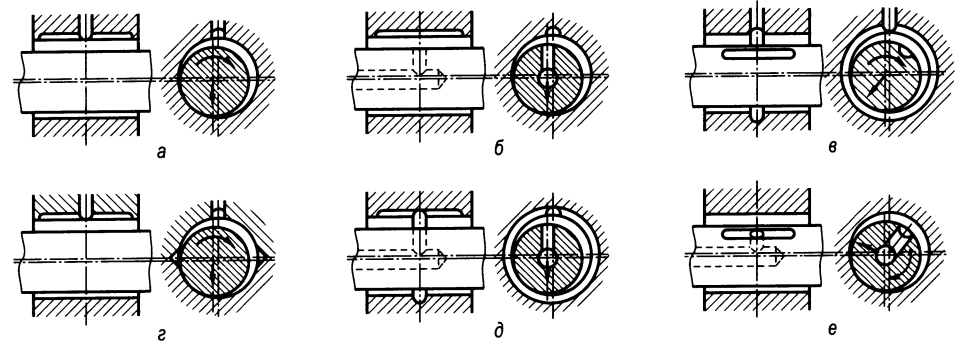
Способы подачи СМ в горизонтальный подшипник через неразъемный корпус и втулку (а, в), через вал (б, д, е) и через разъемный корпус и вкладыш (з):
